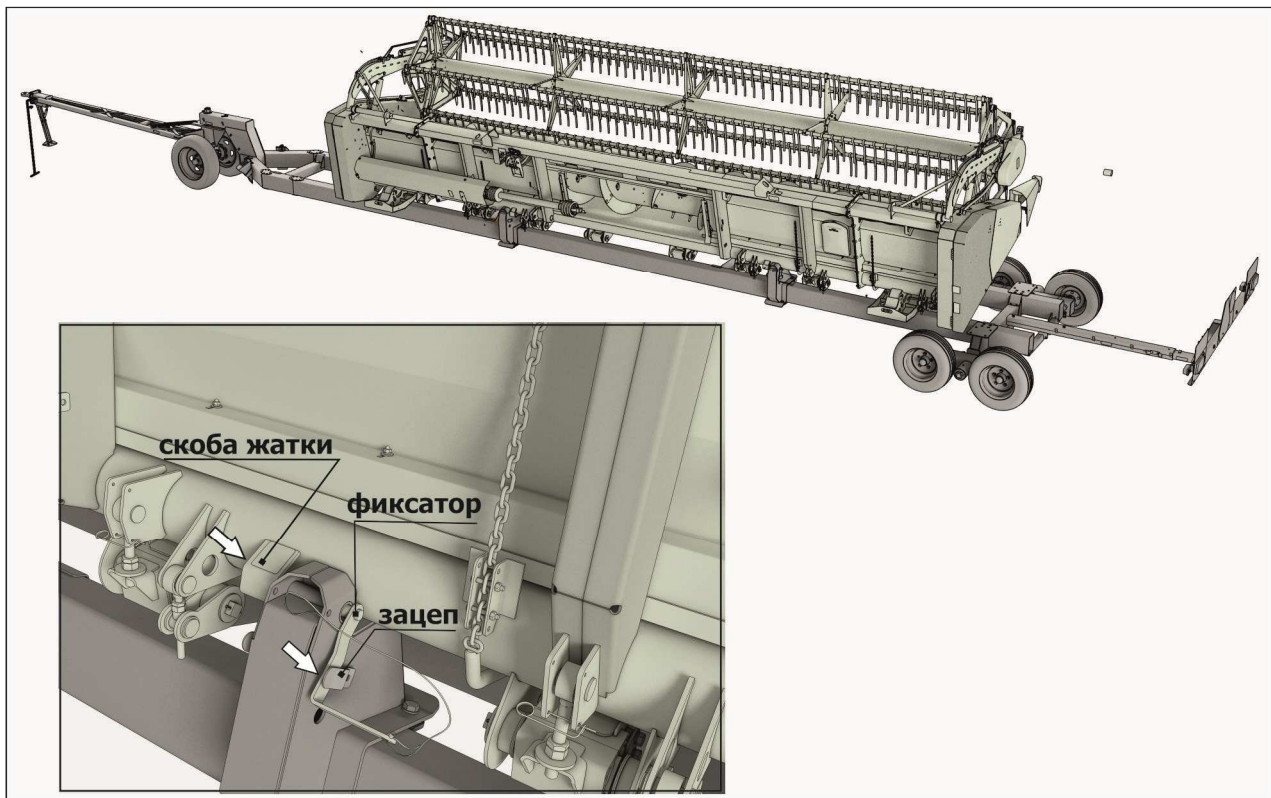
Установка жатки на приспособление ППА-4000-02
